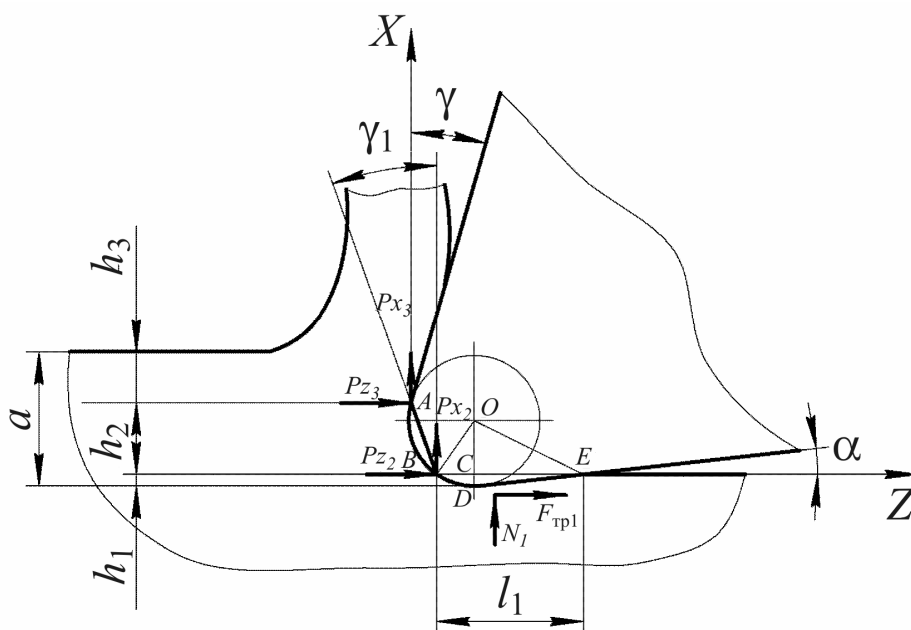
Схема распределения припуска для инструмента со скругленной режущей кромкой
